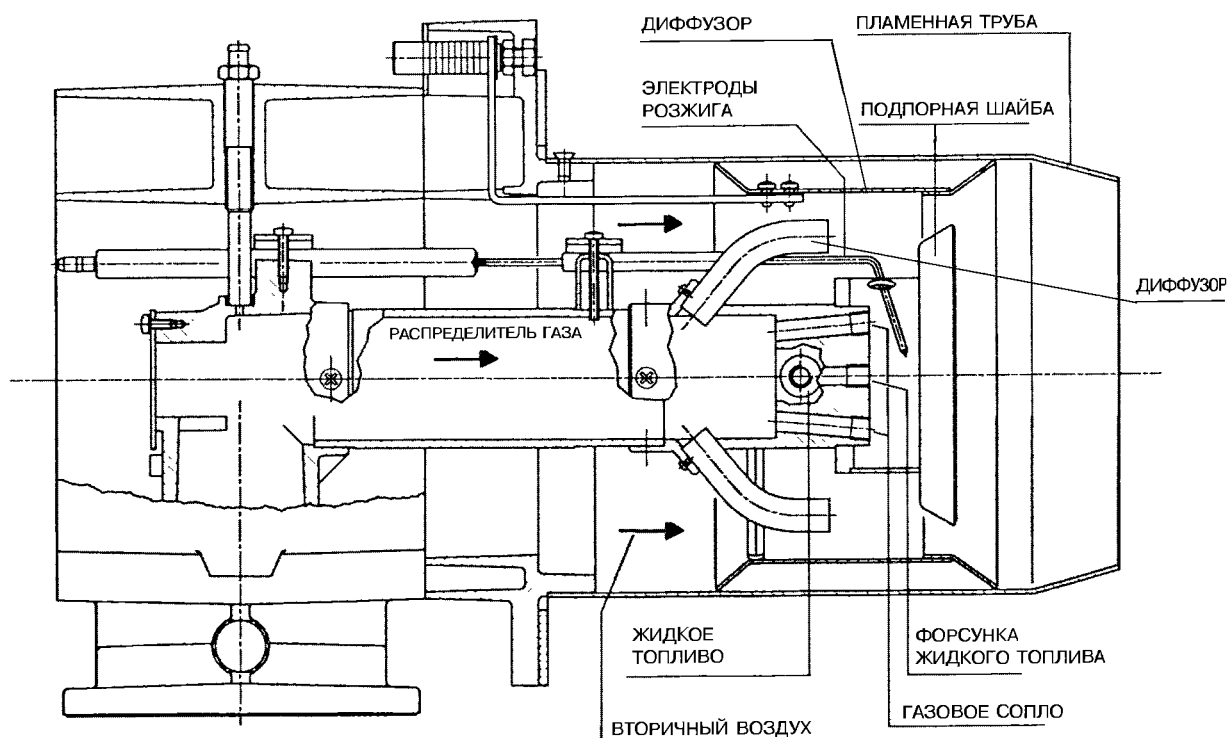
Чертеж головки комбинированной горелки RLS100
